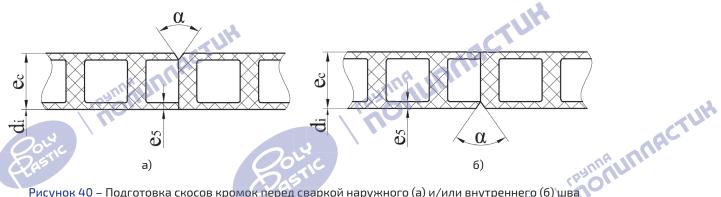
Подготовка скосов кромок перед сваркой наружного (а) и/или внутреннего (б) шва
